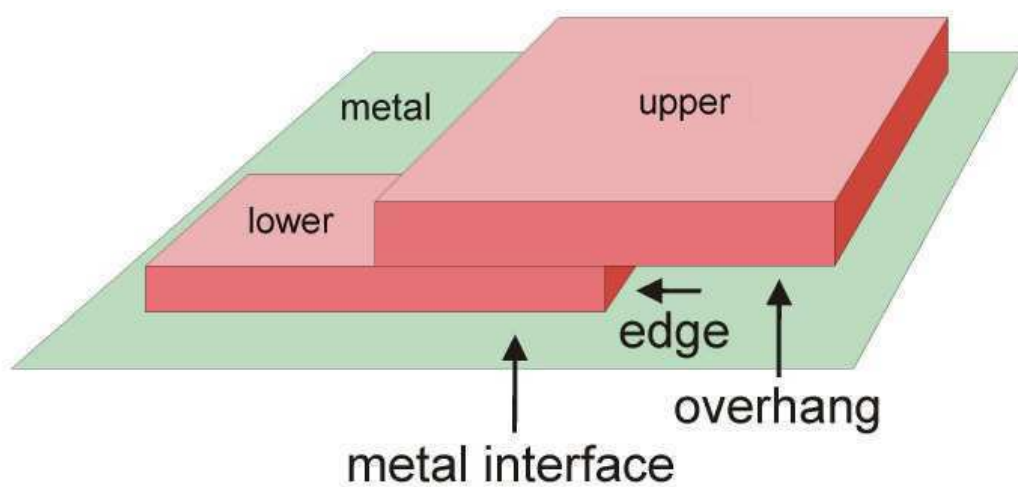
Skizze für einen Druckkörper mit großer überhängender Fläche.
